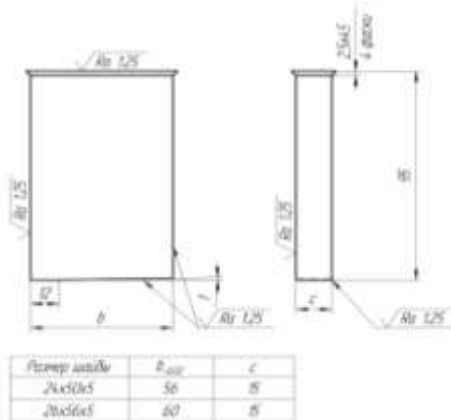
Нож шаговый (усовершенствованная конструкция)
